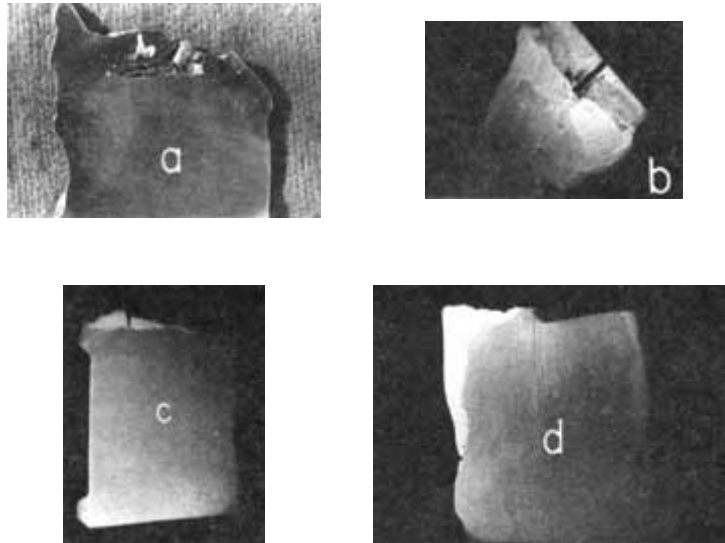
Metalografía de cuatro soldaduras causantes de una fractura. Puede apreciarse que ninguna tuvo corte de biselés. En (a) se observa una enorme grieta rellena de escoria y en (b) se formó una grieta en la zona reblandecida por el calor de la soldadura. En (c) y (d) hay, además, insuficiencia de material de aporte del electrodo.
